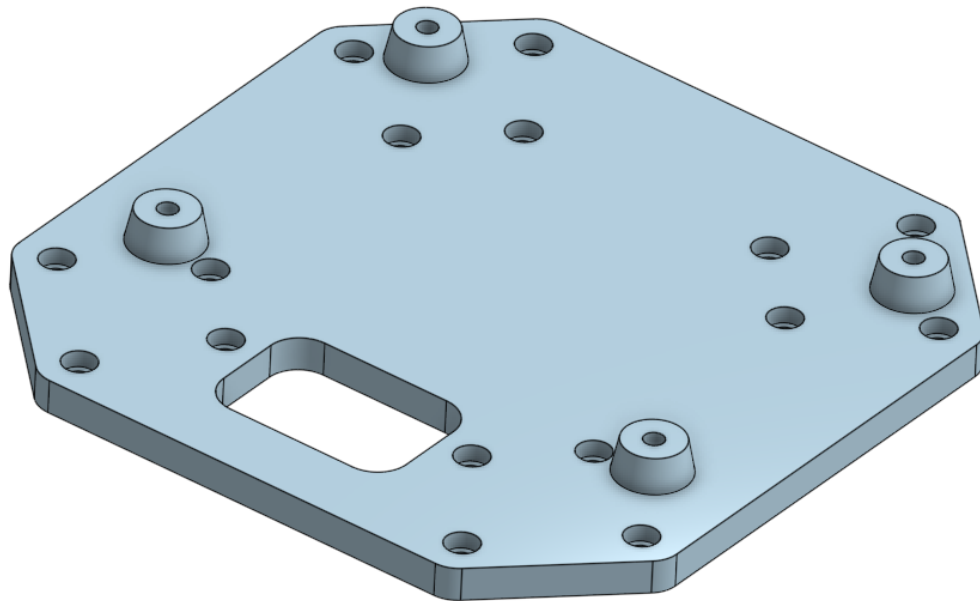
Vista isométrica del diseño del adaptador para *Flight Controller Test Kit* del Kit F450
